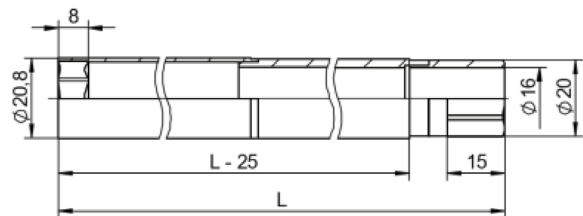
Montageschlüssel Typ 1300A4SP100-400
